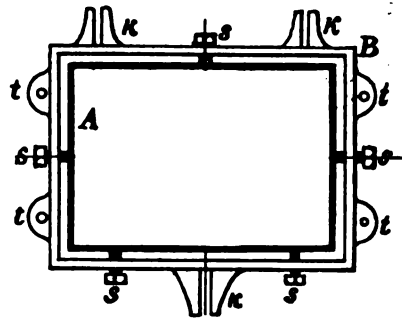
A Blindrahmen, B Formkasten, K Ansätze zur Befestigung des Kastens an der Modellplatte, t Schloß, s Klemmschrauben für A.
